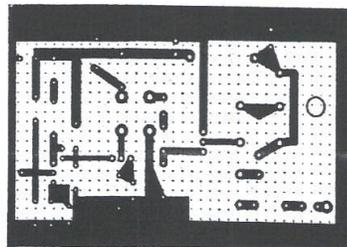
PLACA DE FIXAÇÃO IMPRESSA DO MÓDULO EXCITADOR
